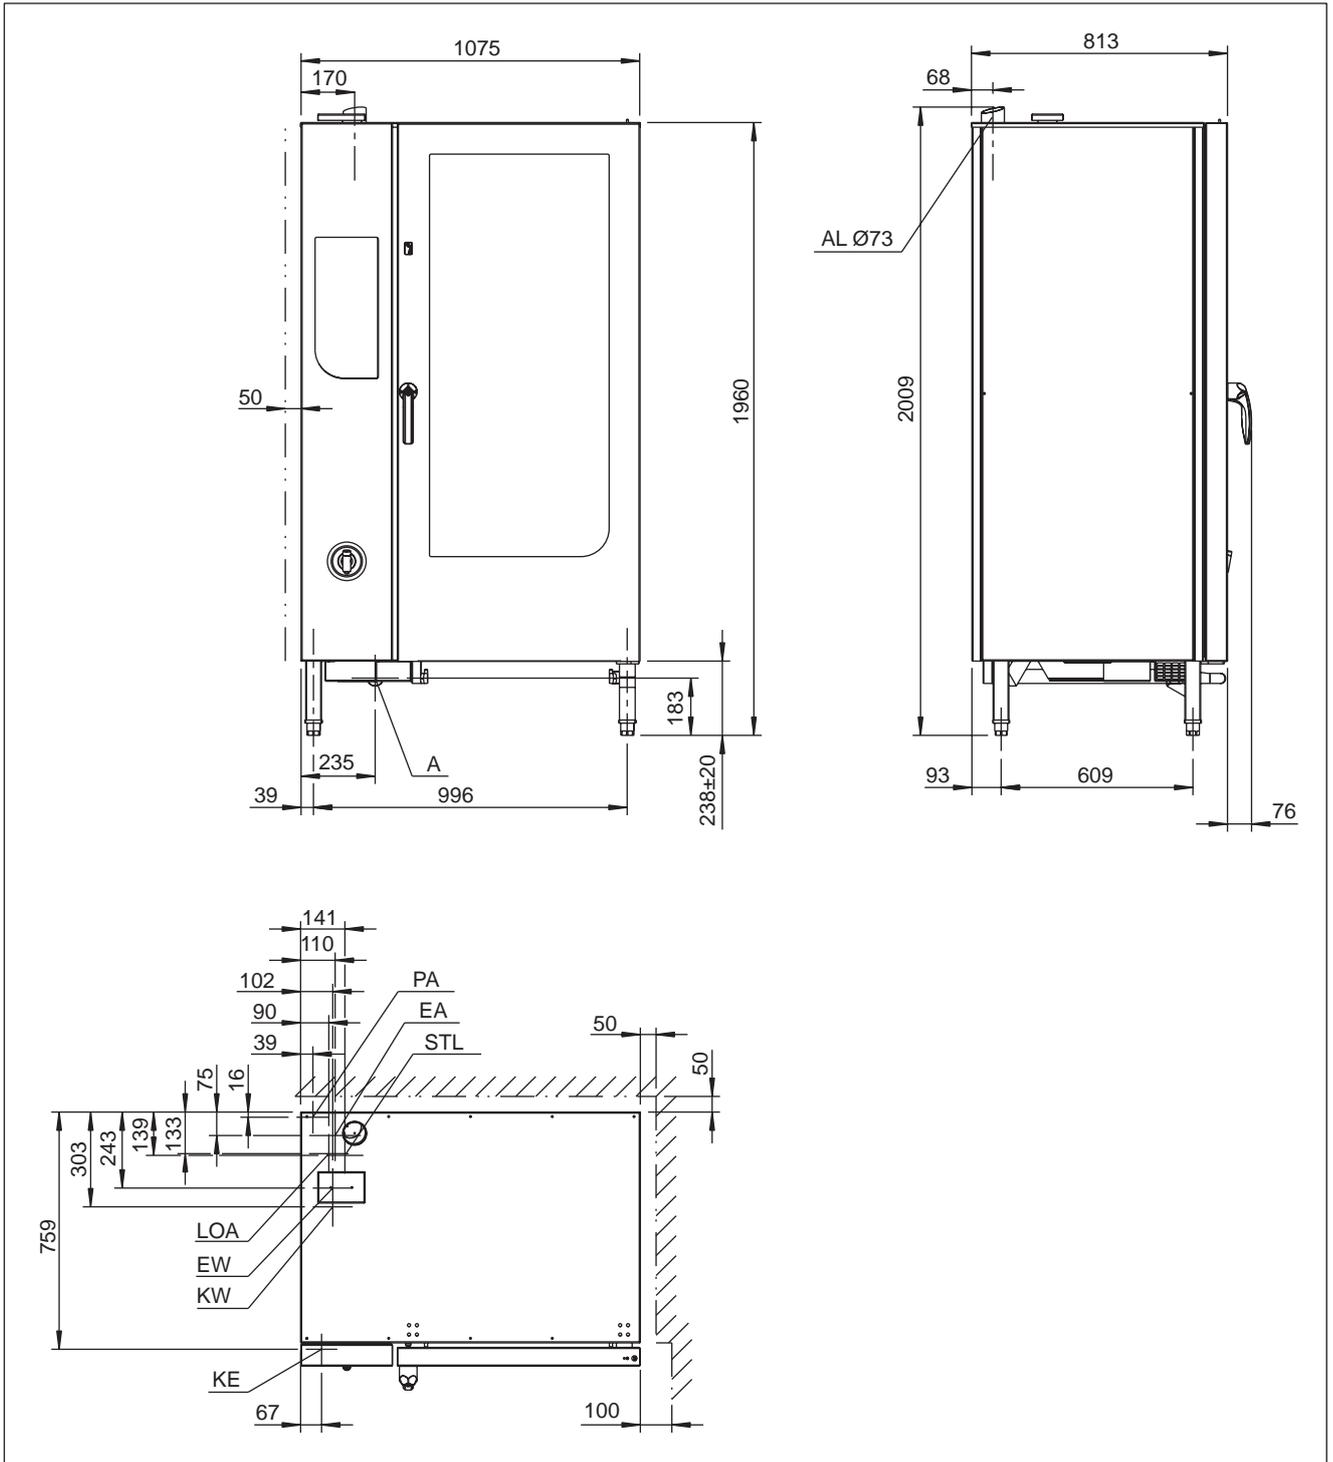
Combi-cuiseurs Henny Penny 215/220, dimensions en mm
